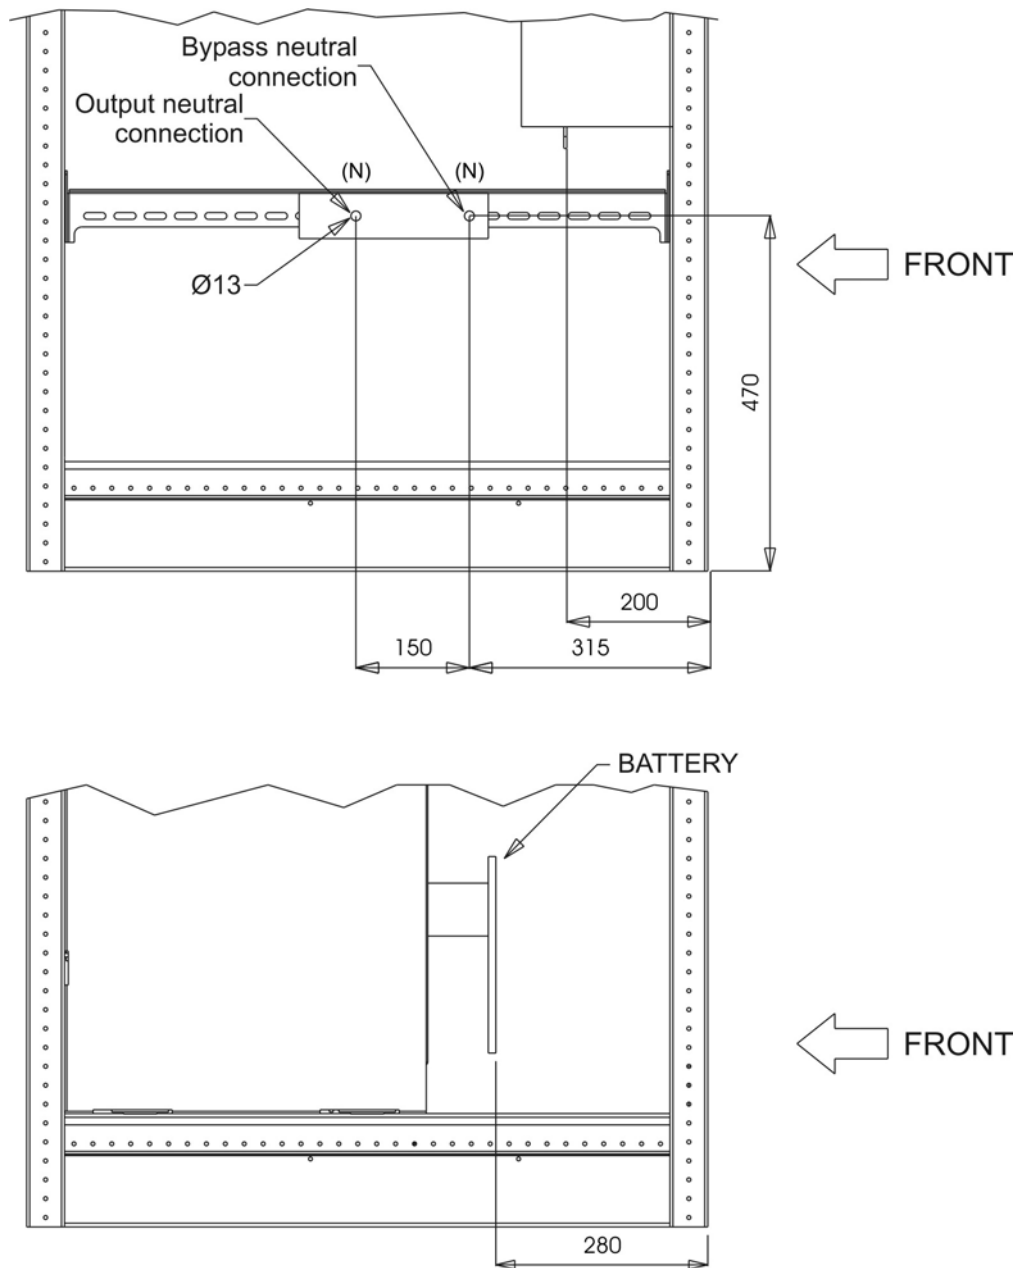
Vue latérale du bornier du KEOR HP 400 kVA
